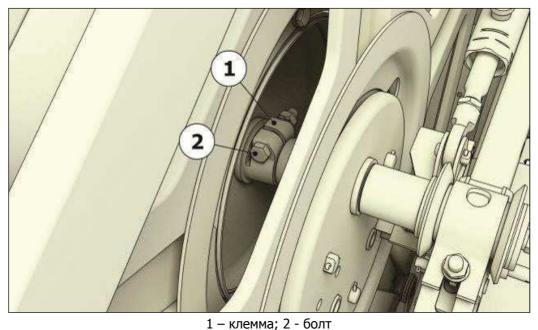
Контроль затяжки клеммы мотовила
